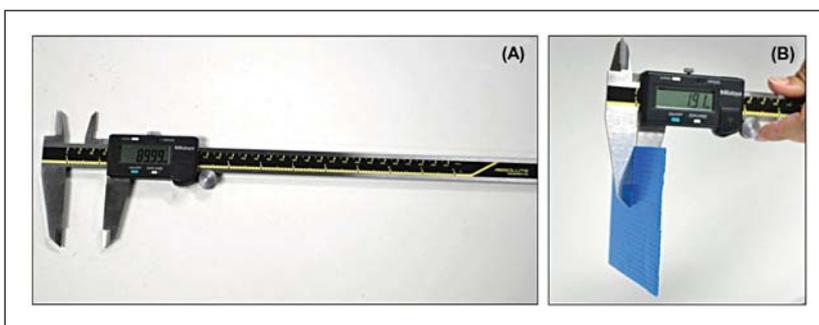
Paquímetro (A) e medição da espessura de um plástico corrugado (B).
